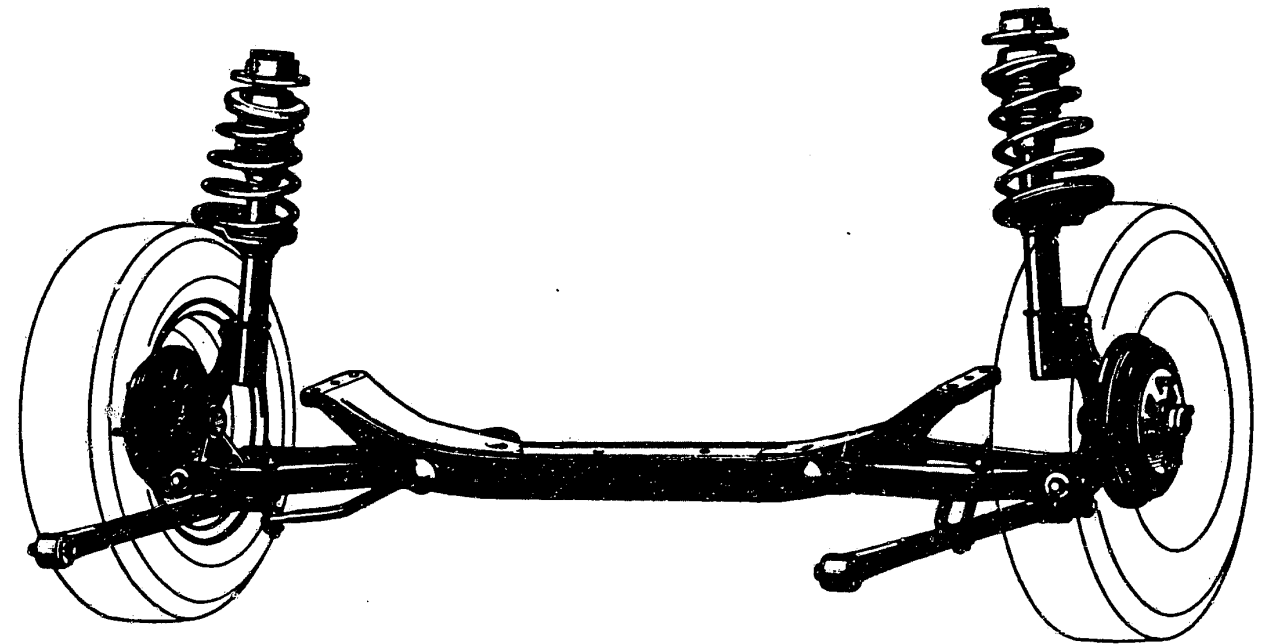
Auch die Hinterräder sind einzeln aufgehängt. Die Schraubenfedern der Federbeine sind asymmetrisch angeordnet. Längs- und Parallelquerlenker übernehmen die Radführung.
